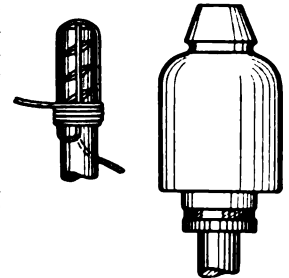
Holländischer Stützengewindeumwicklung. Bild 2. Englische Isolatorbefestigung.
